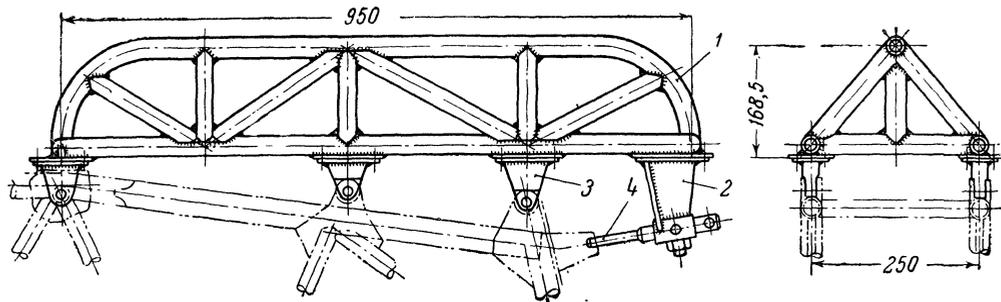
Приспособление для установки ушков на раме фюзеляжа.
